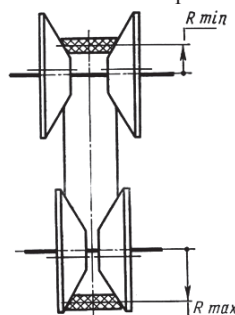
Схема вариаторов с гибкой связью и параллельными приводными валами
